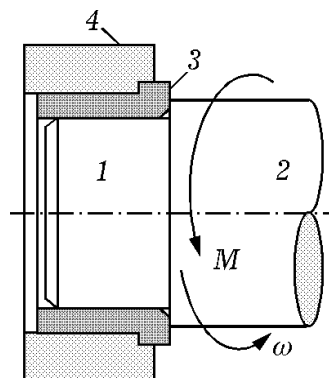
Схема вращения цапфы вала относительно вкладыша подшипника: 1 — цапфа вала; 2 — вал; 3 — вкладыш подшипника скольжения; 4 — подшипник скольжения
